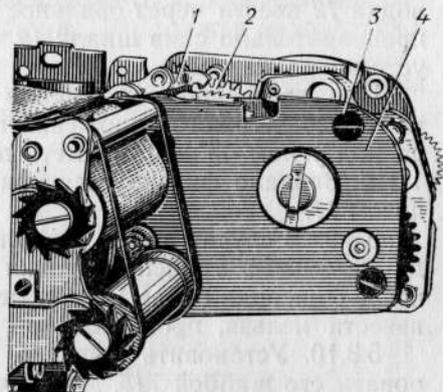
Механизм транспортировки на корпусе зеркала (вид снизу):
